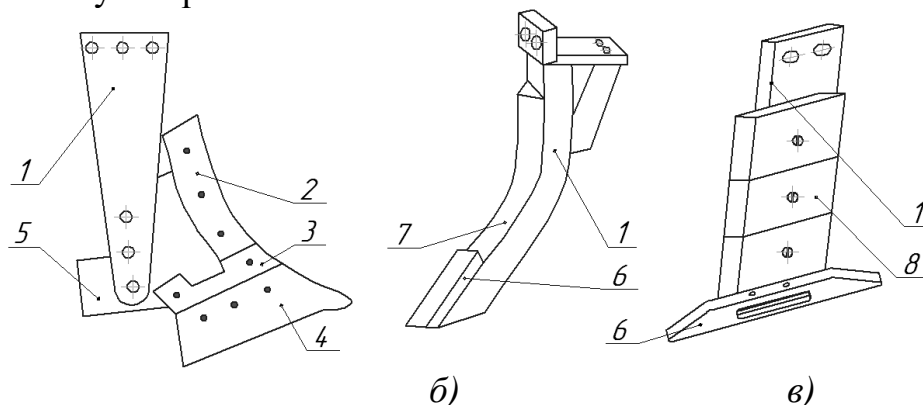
Корпуса плугов для безотвальной вспашки: а) корпус Мальцева; б) чизельный плуг; в) корпус «Параплау»
